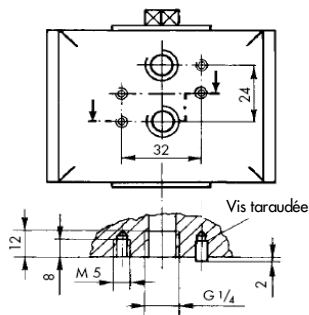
· Plan de pose NAMUR 1/4" (dimensions en mm)
